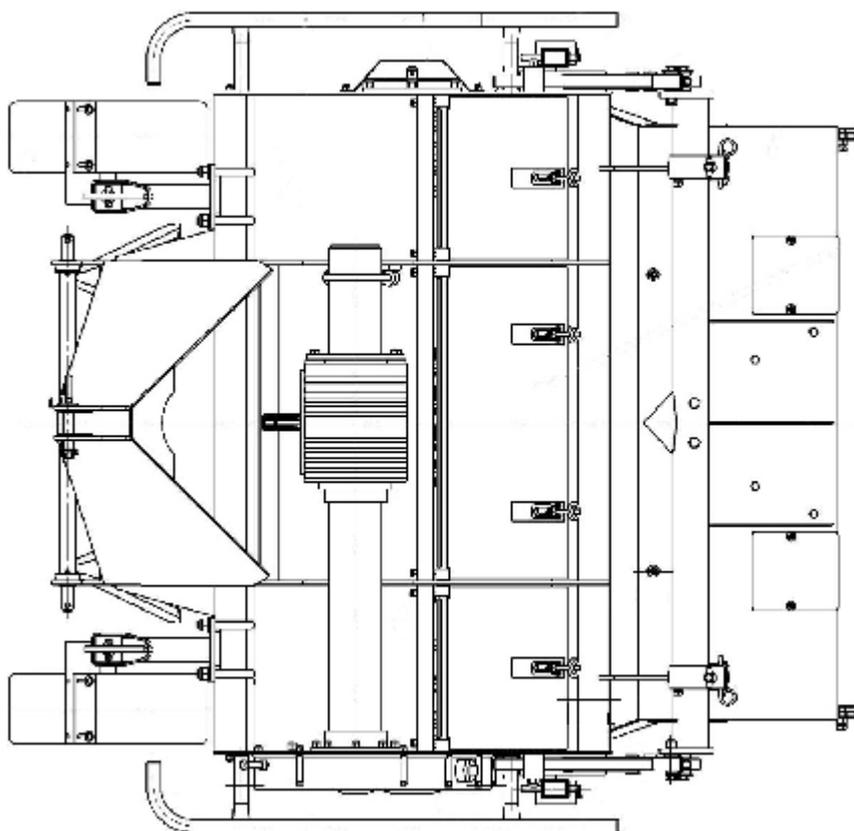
Культиватор-гребнеобразователь (вид сверху)
